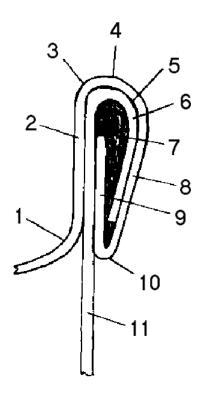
Конструкция двойного закаточного шва: 1 – внутренний радиус;
